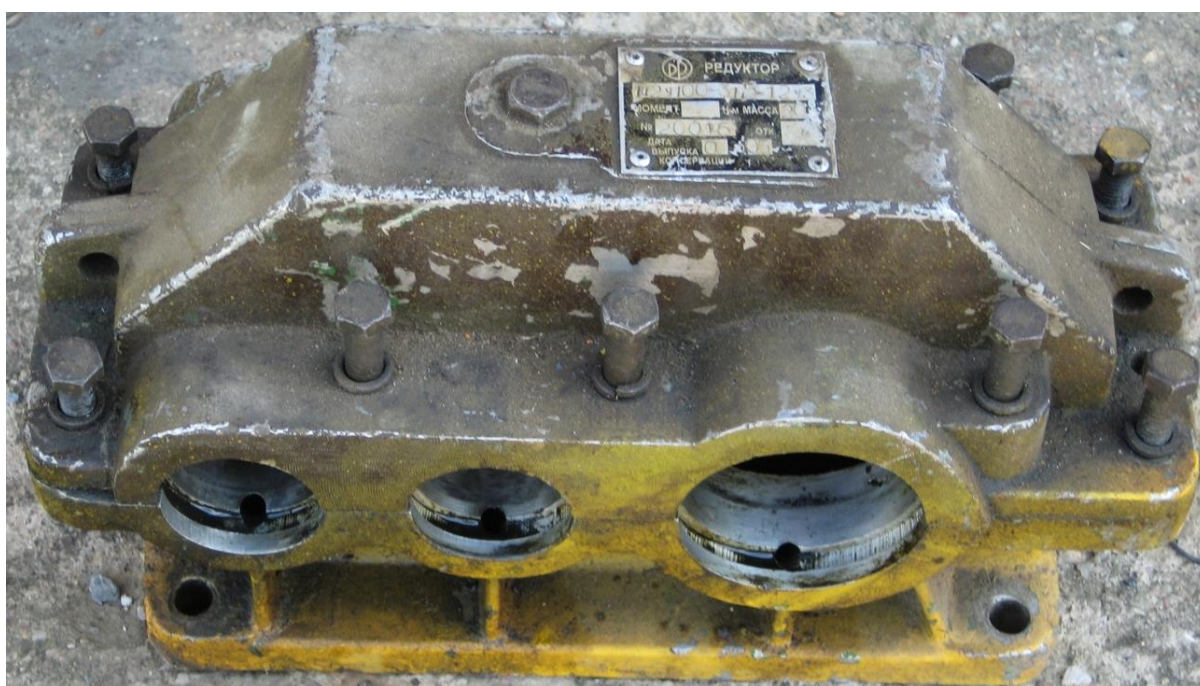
Корпус и крышка цилиндрического редуктора.
